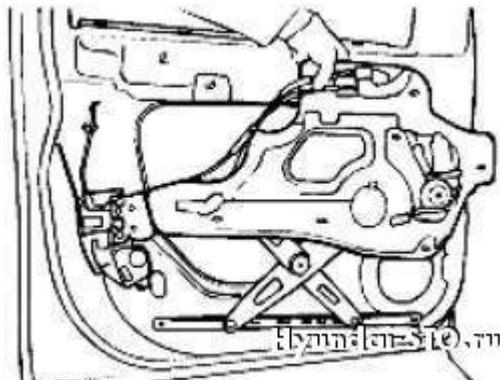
(#) Demontáž přední a zadní sklo průvodce drážky dveří
